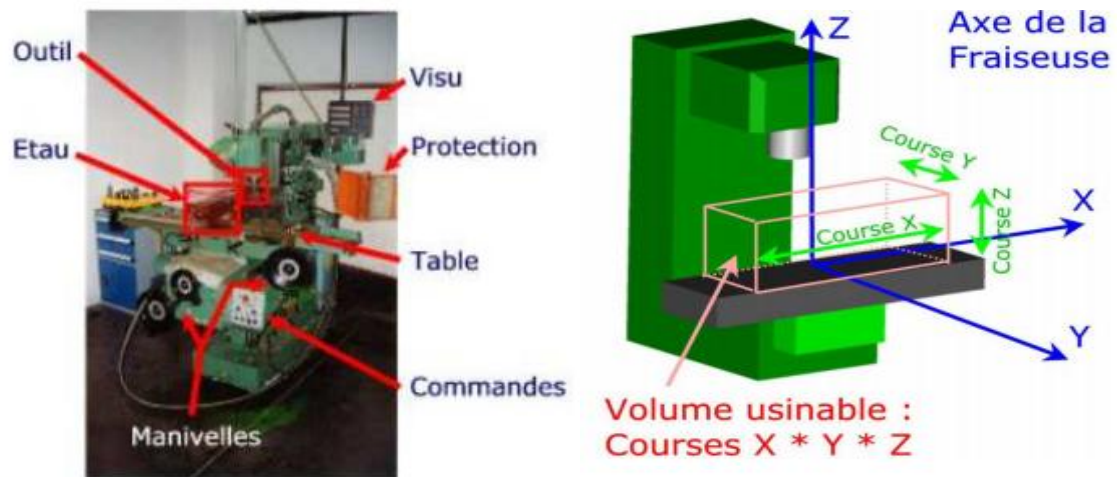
Le principe de fonctionnement d'une machine-outil de fraisage [3].
